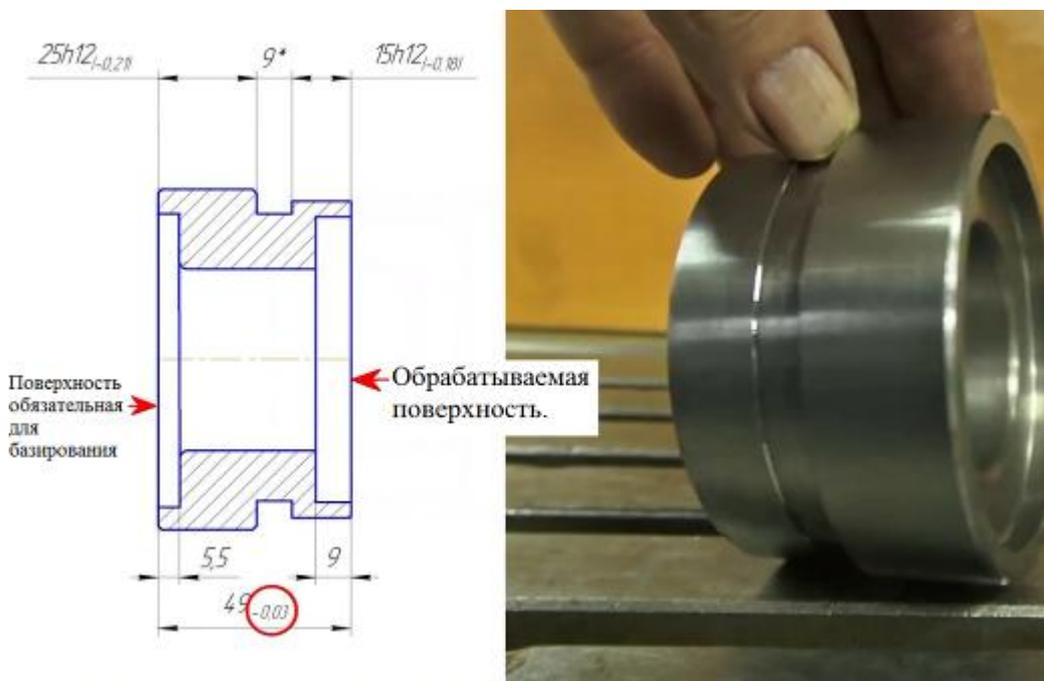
Выбор для детали поверхности для базирования условиями чертежа
